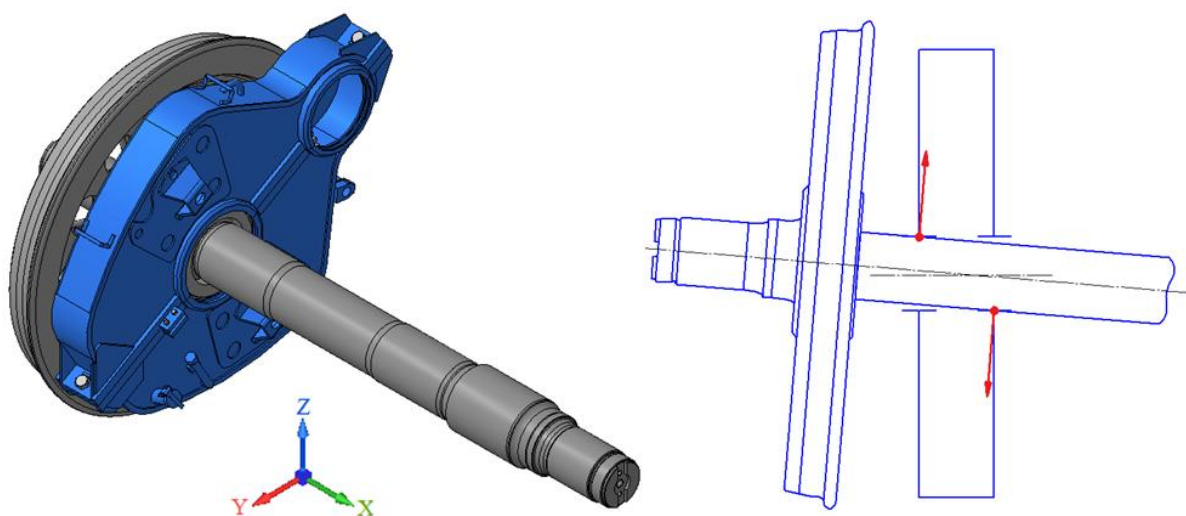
Условная схема нагружения кожуха зубчатой передачи при вписывании тележки в кривую
